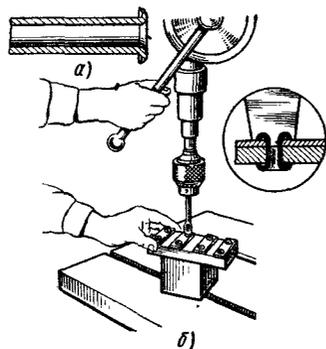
Развальцовка головки пустотелой заклепки на сверлильном станке:
